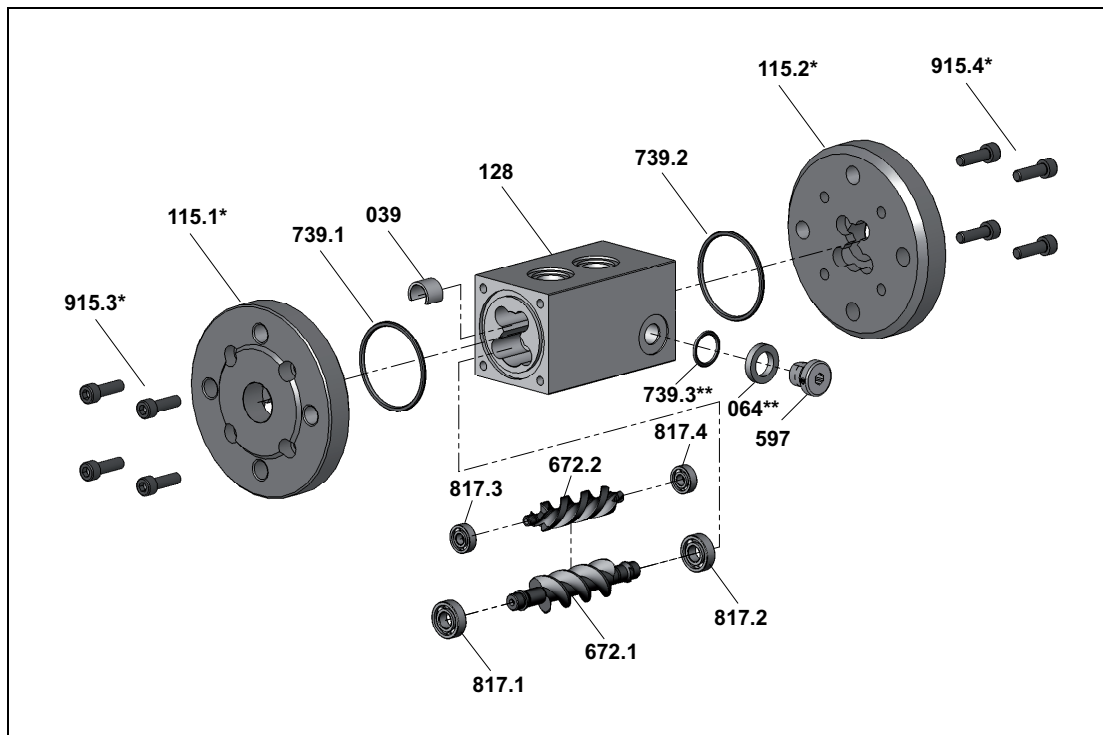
Explosionszeichnung OME 13 – 52 Flanschanschluss
